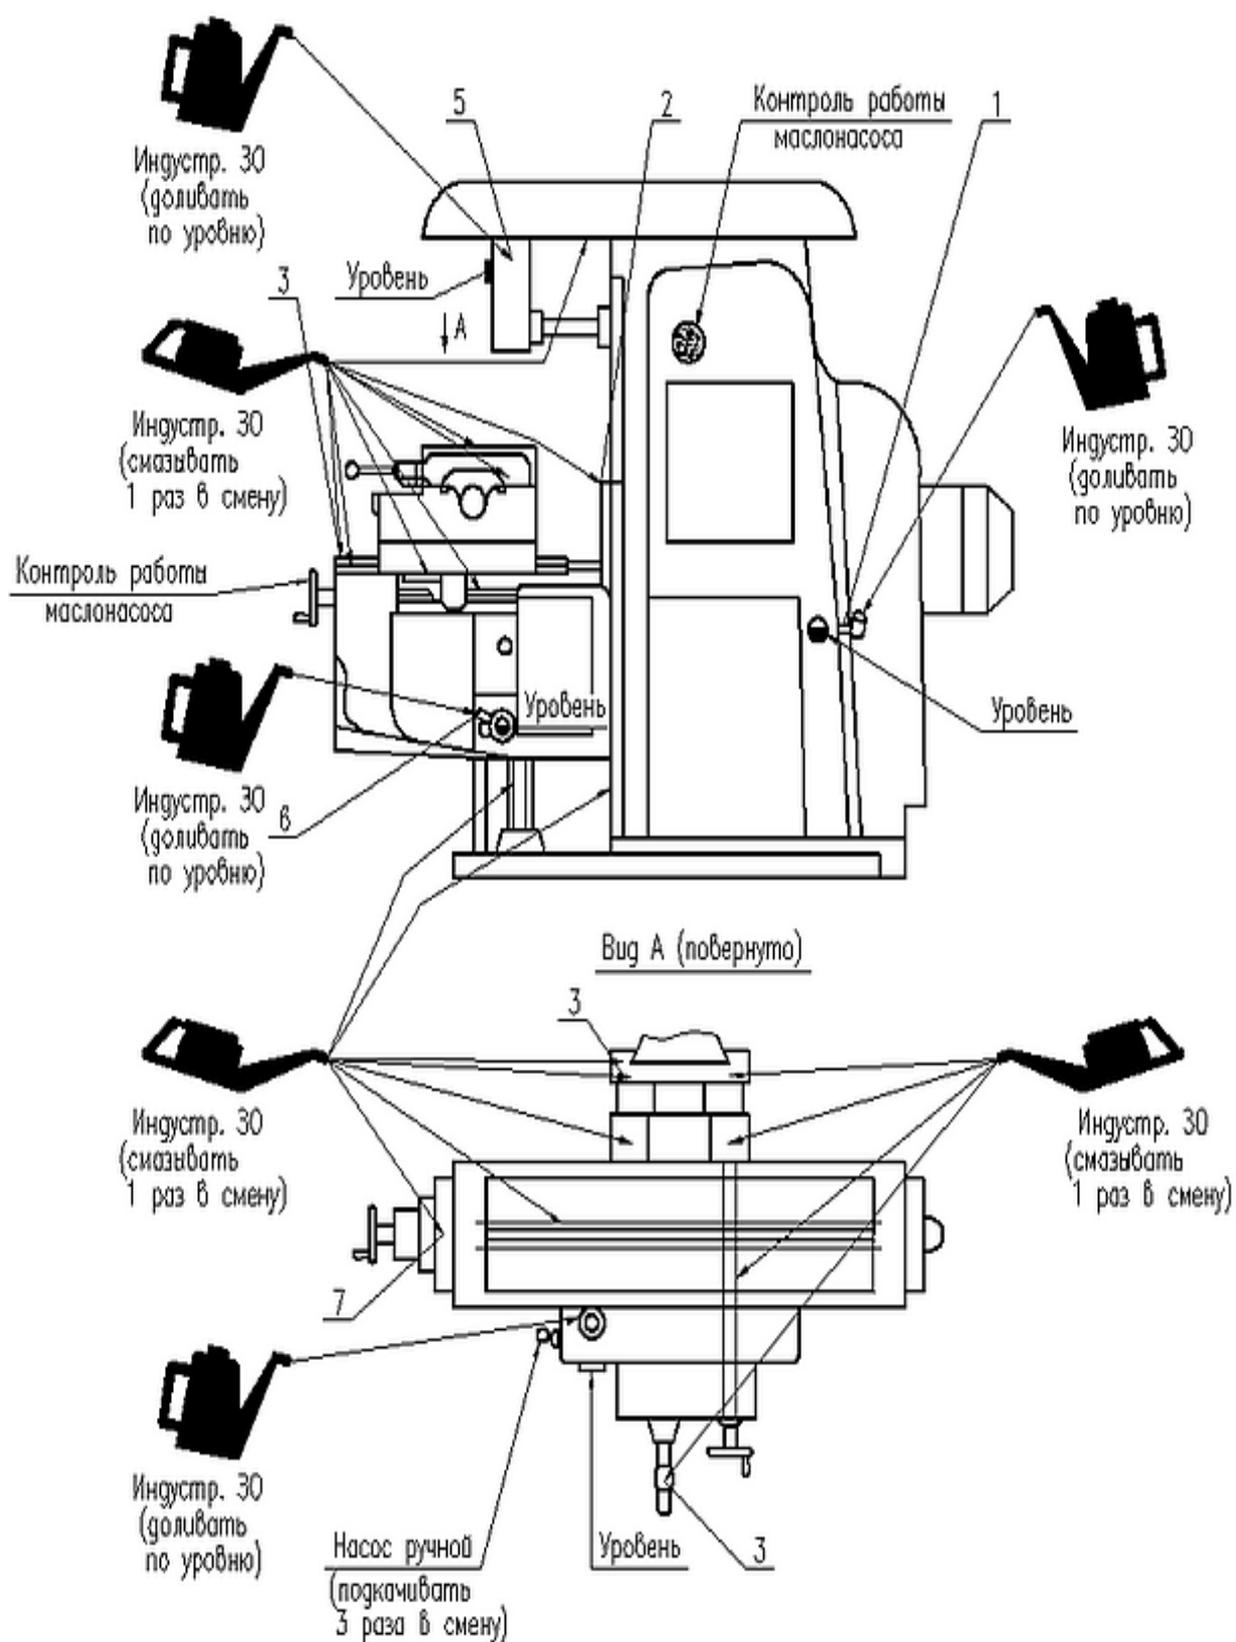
Схема смазки горизонтально-фрезерного станка модели 6М82
